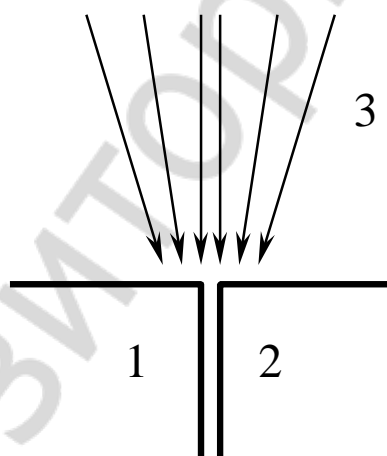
Фокусировка излучения при лазерной сварке:
